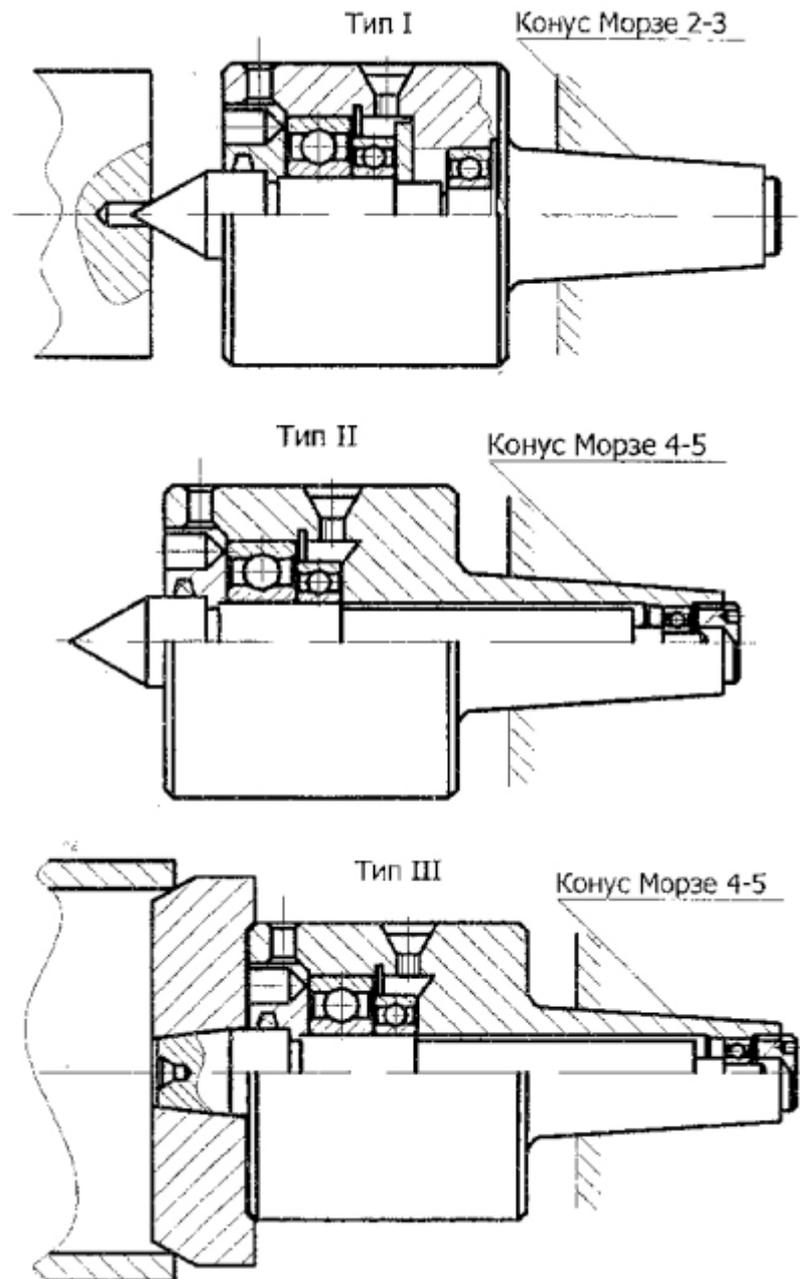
Конструкции вращающихся центров: тип I и II – для установки заготовок по центровым отверстиям; тип III – для установки полых деталей.
